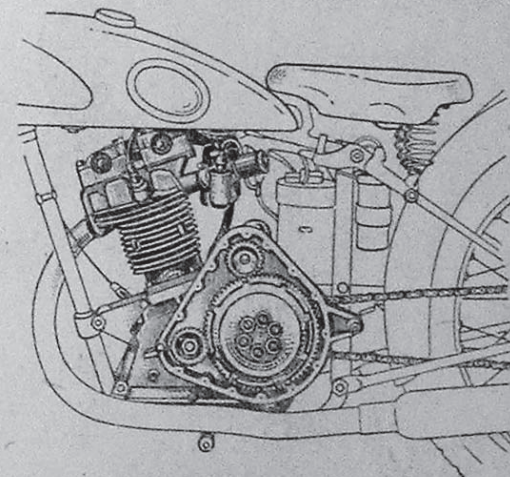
б). Шестеренная передача от двигателя к коробке передач, с промежуточной паразитной шестерней.
